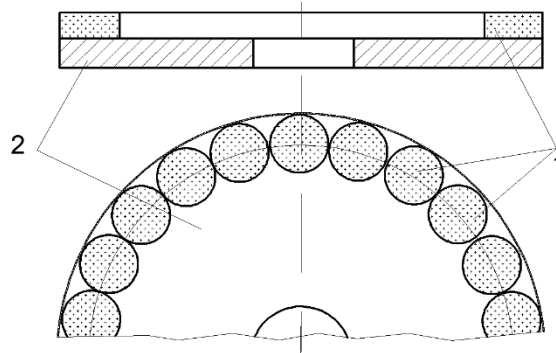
Збірний алмазний круг для торцевого шліфування неметалевих матеріалів підвищеної твердості:
